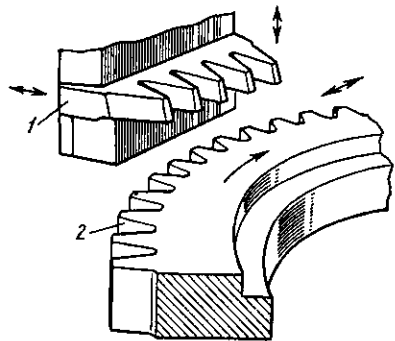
Схема нарезания зубьев зубчатыми гребенками
